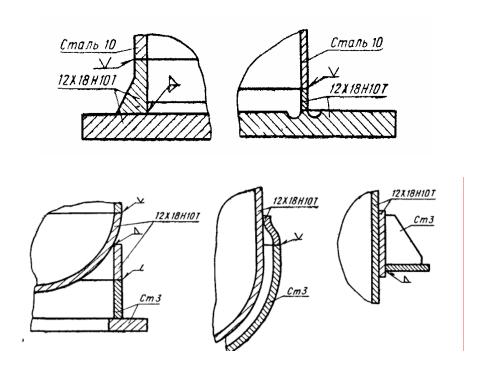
Узлы сварки элементов из коррозионностойких и углеродистых сталей с промежуточными деталями
